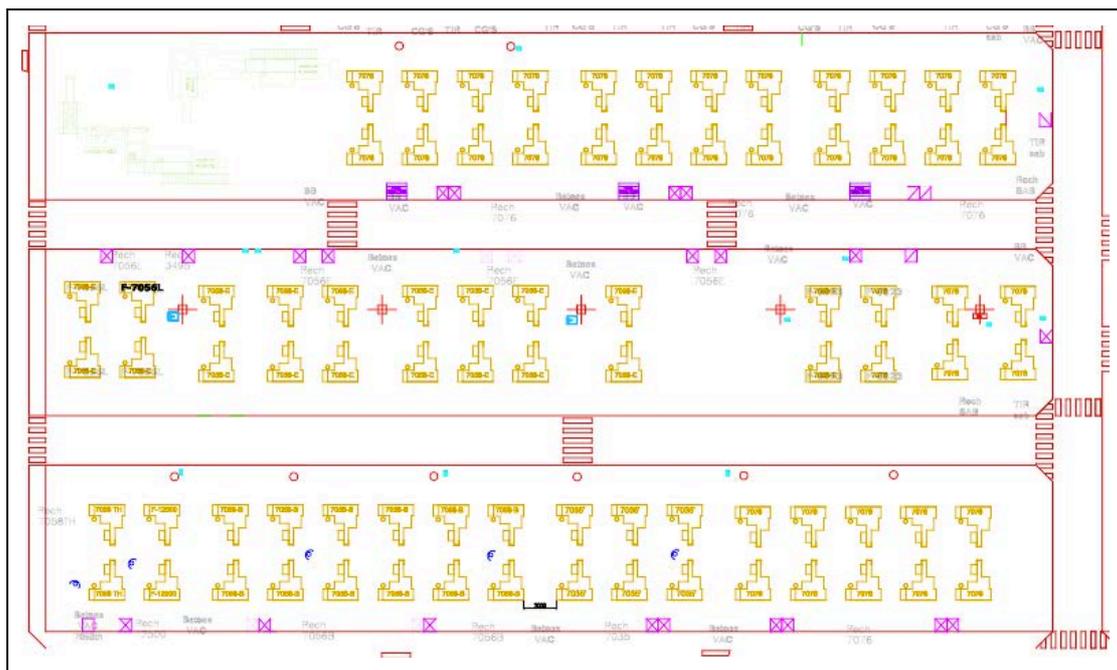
Plano detalle de la zona 2 de liadoras. [Fuente: Elaboración propia]
